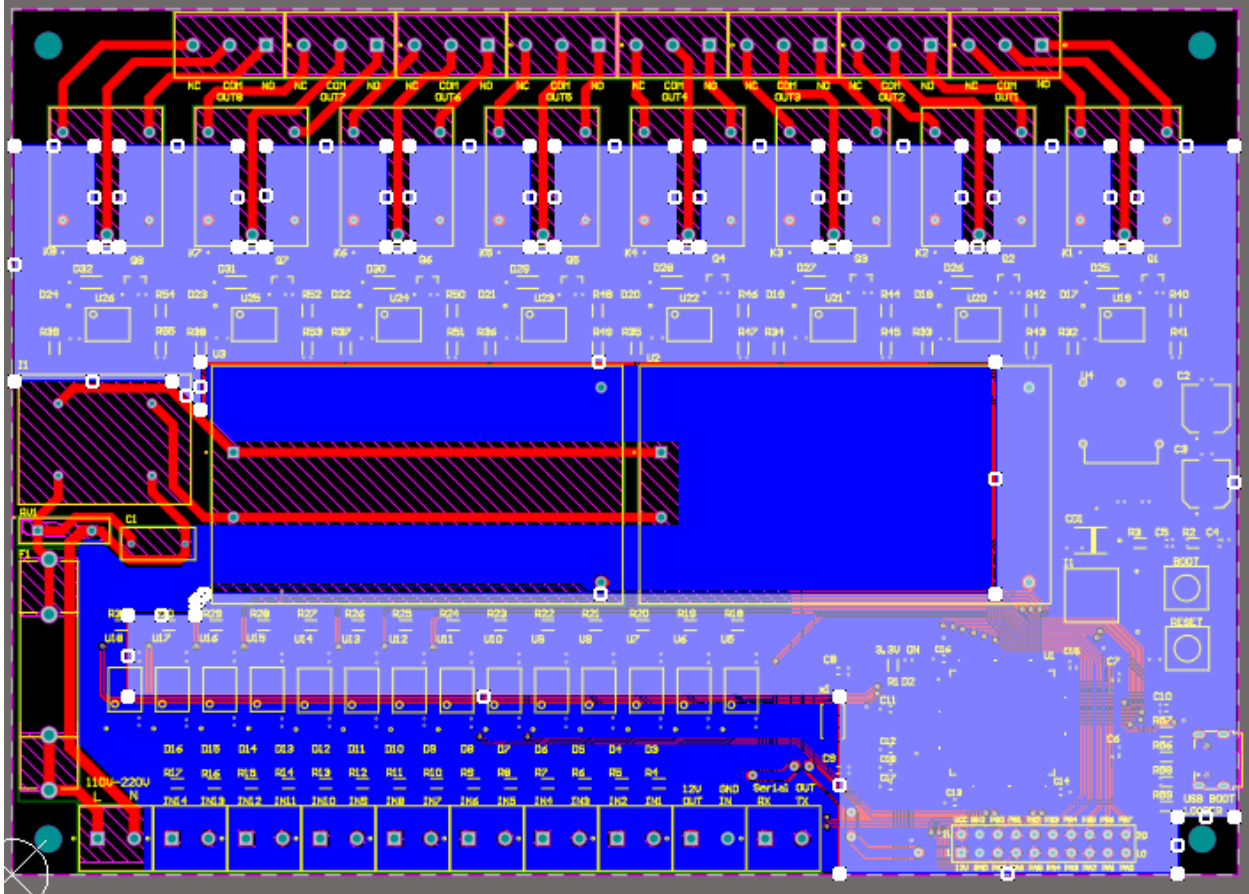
Polígonos de voltaje ubicados en la capa superior del PCB.
